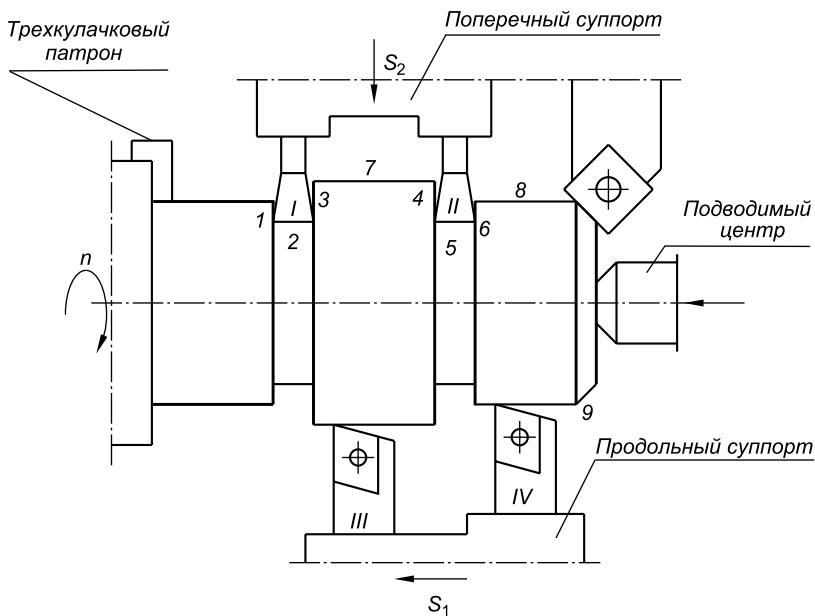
Параллельная концентрация операции токарной обработки вала: 1—9 — параллельно обрабатываемые поверхности вала; I—IV — обрабатывающие инструменты;  $S_1$  и  $S_2$  — подача суппортов;  $n$  — вращение вала
